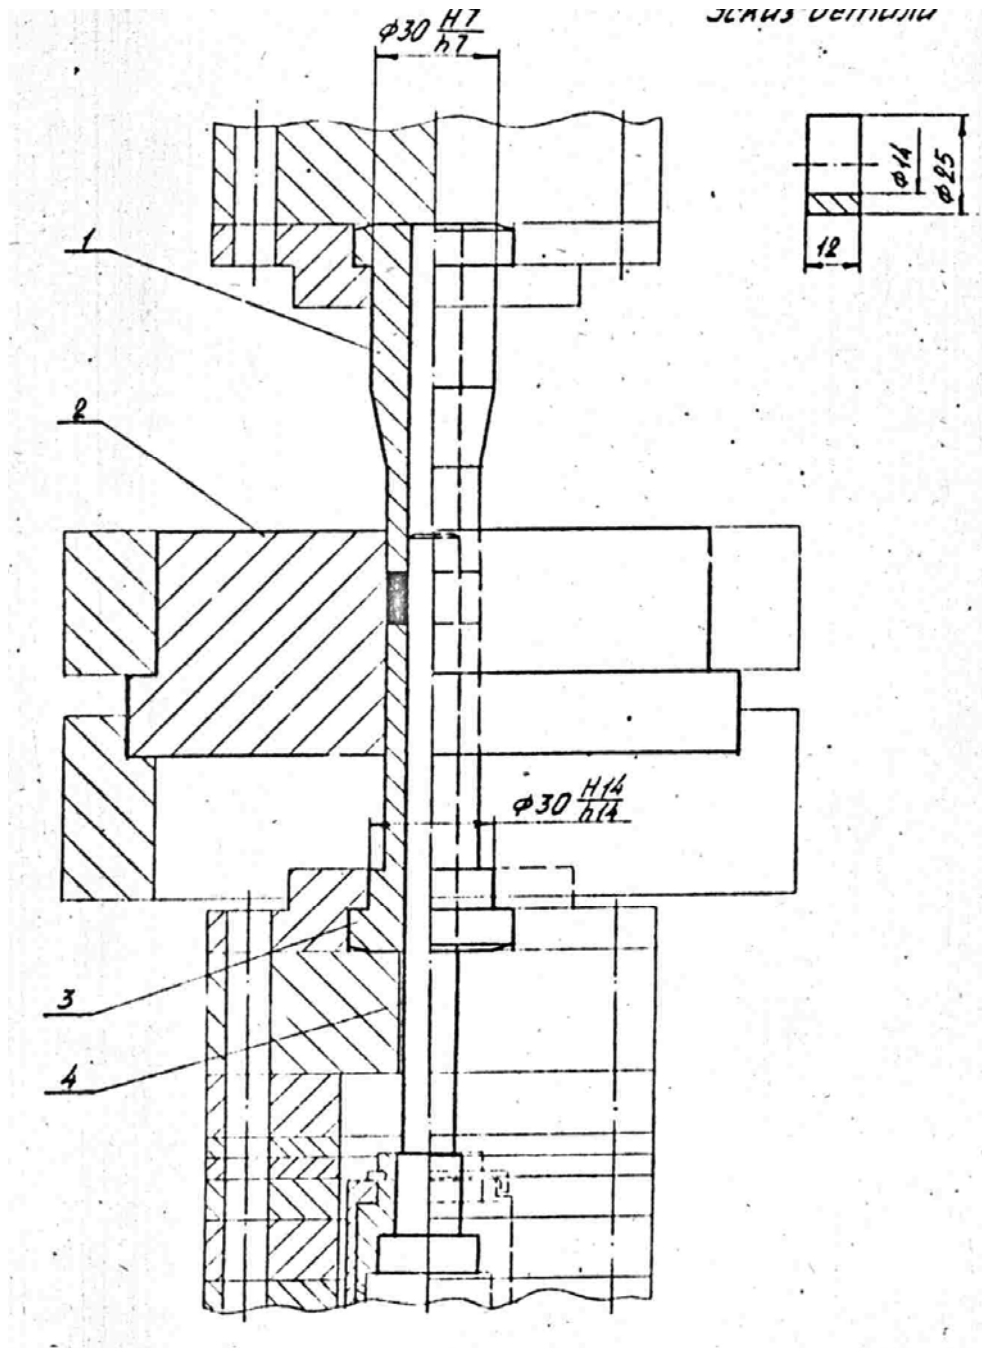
Конструкция рабочих частей пресс-форм (матрица, пуансон, стержень) для прессования изделия цилиндрической формы с внутренним отверстием
